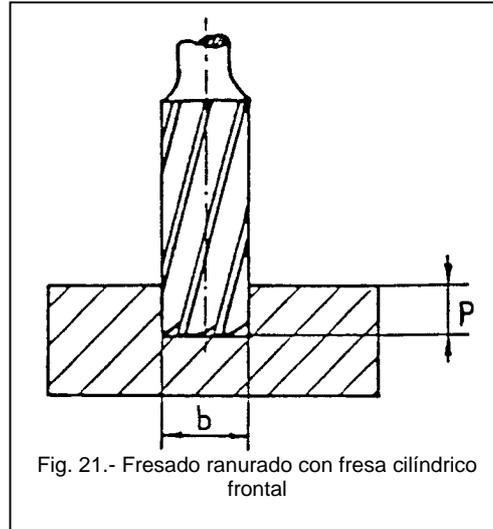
Fresado ranurado con fresa cilíndrica frontal
